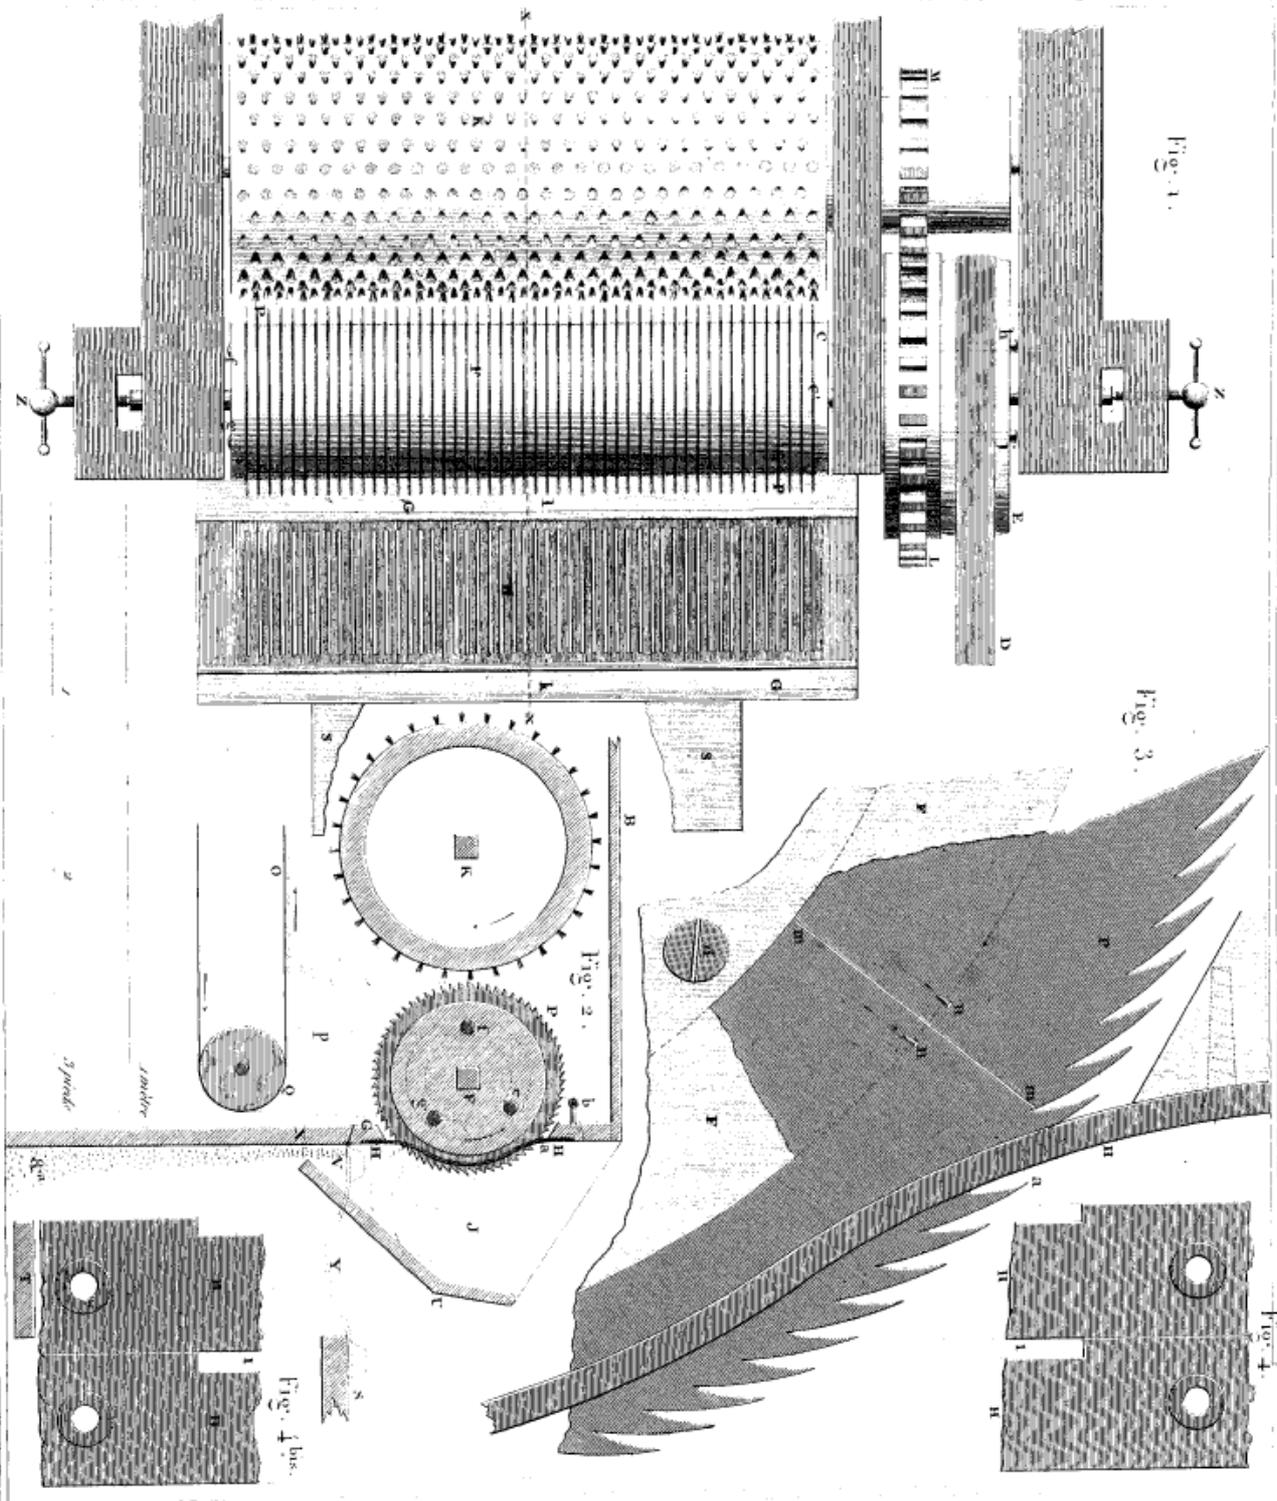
Plan du moulin, le plancher B étant enlevé, et le cadre G des barreaux H étant abaissé.
